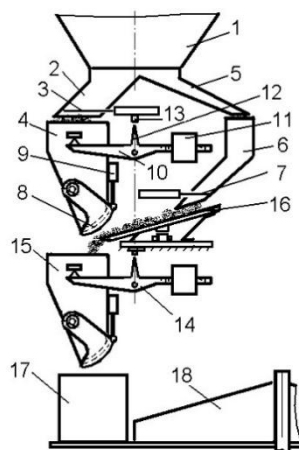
Дозатор двукратного взвешивания с рычажными весовыми устройствами.
